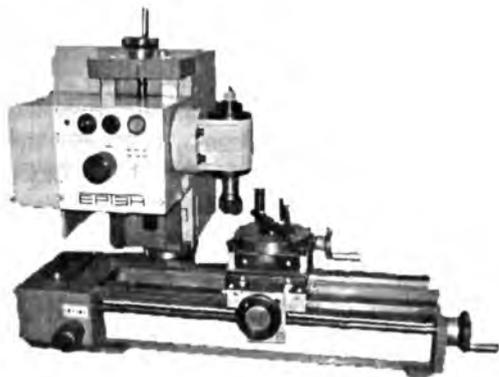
Настройка установки на станок вертикально-фрезерной головки
